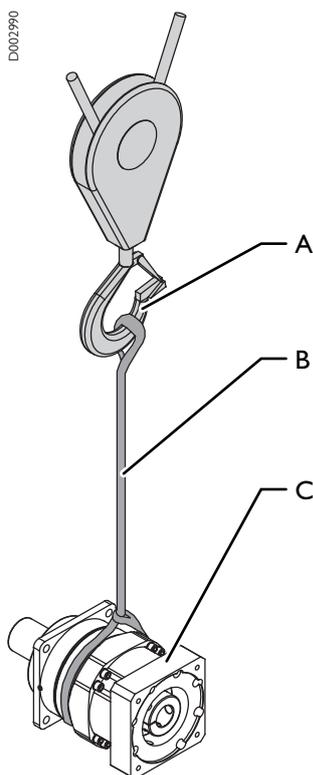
Зачалить такелаж: Планетарный редуктор
